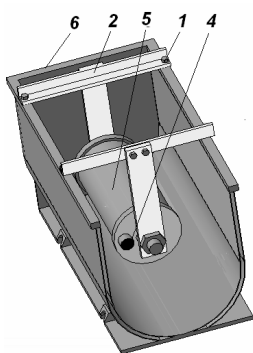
Конструкция рабочей камеры для ВиАУЗО деталей в свободном состоянии с расположением ультразвукового преобразователя у дна рабочей камеры: 1 – резьбовые соединения; 2 – крепление; 4 – штуцер для подачи охлаждающей жидкости; 5 - ультразвуковой преобразователь; 6 - рабочая камера
